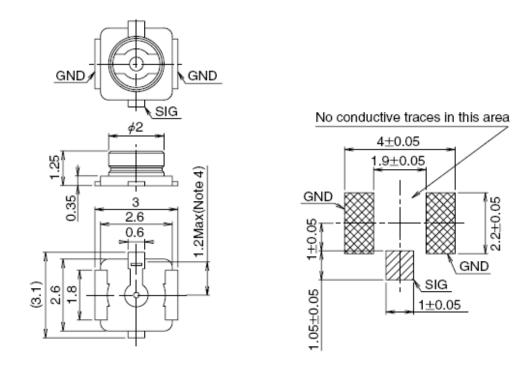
U.FL-R-SMT 连接器尺寸(单位:毫米)
